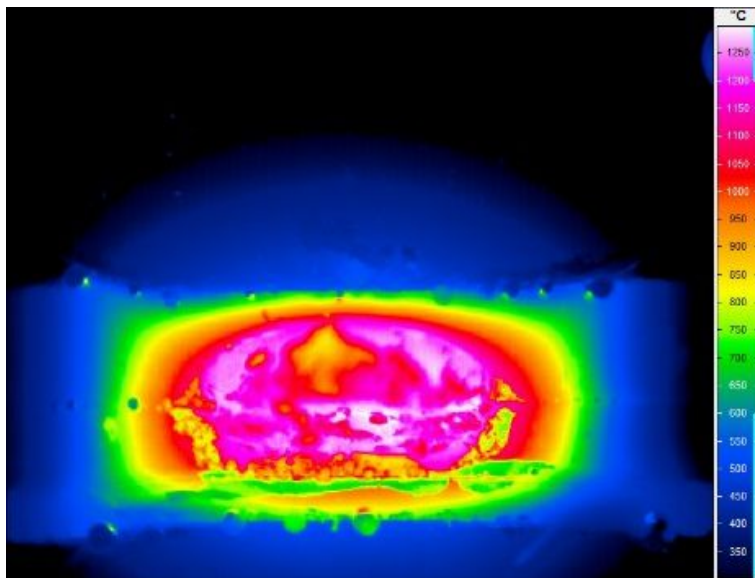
Thermografieaufnahme einer Punktschweißung im Halbschnitt
